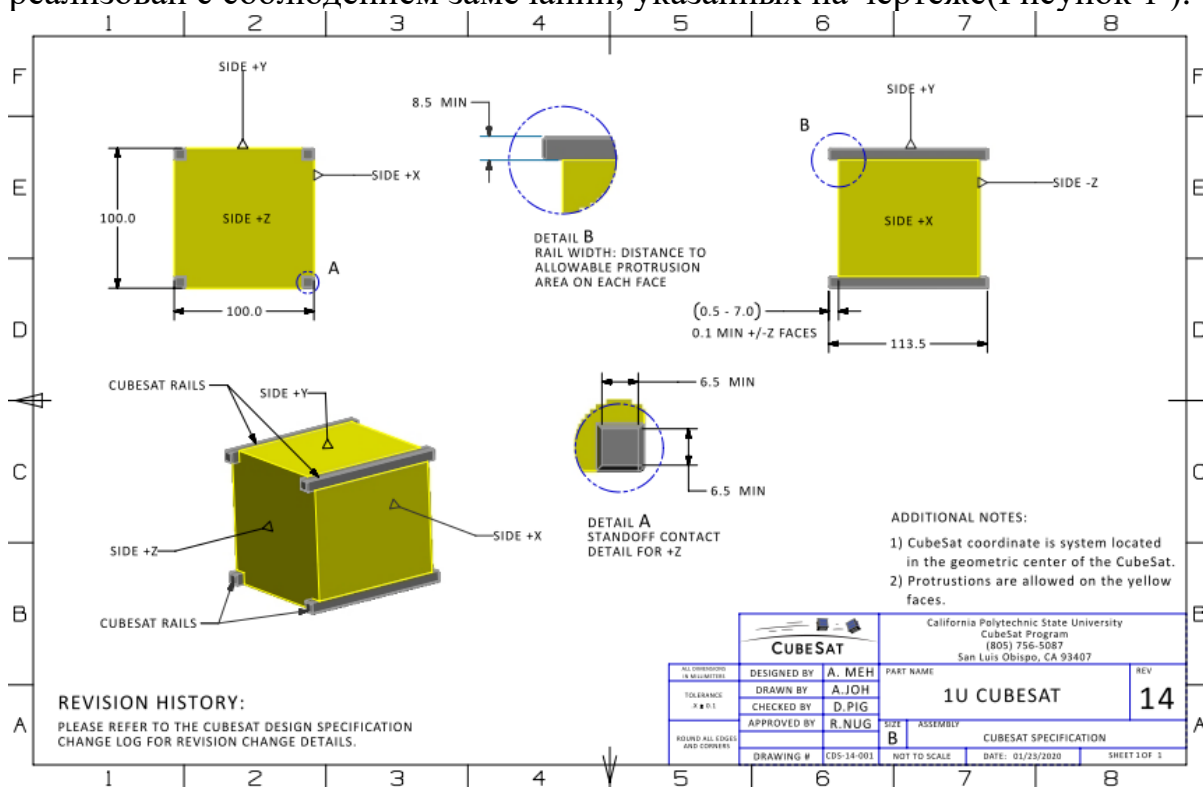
Чертеж спутника формфактора Cubesat 1u.
